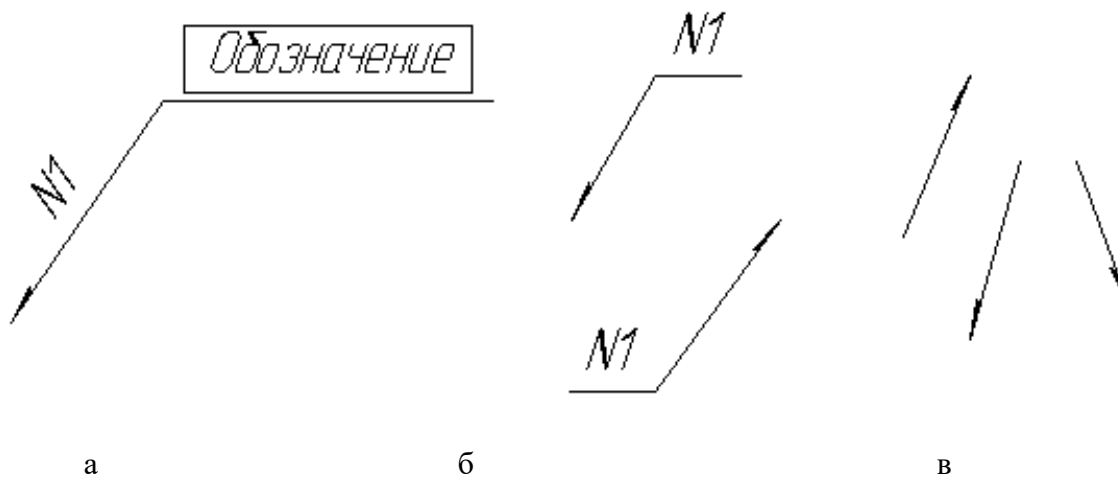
Образец выполнения упрощений обозначений швов сварных соединений.
